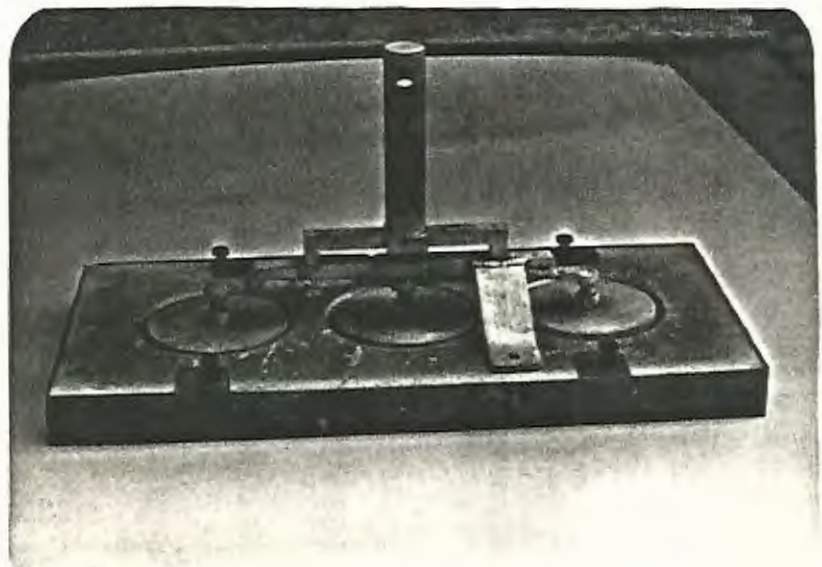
DISPOSITIVO ARMADO. VISTA INF.
